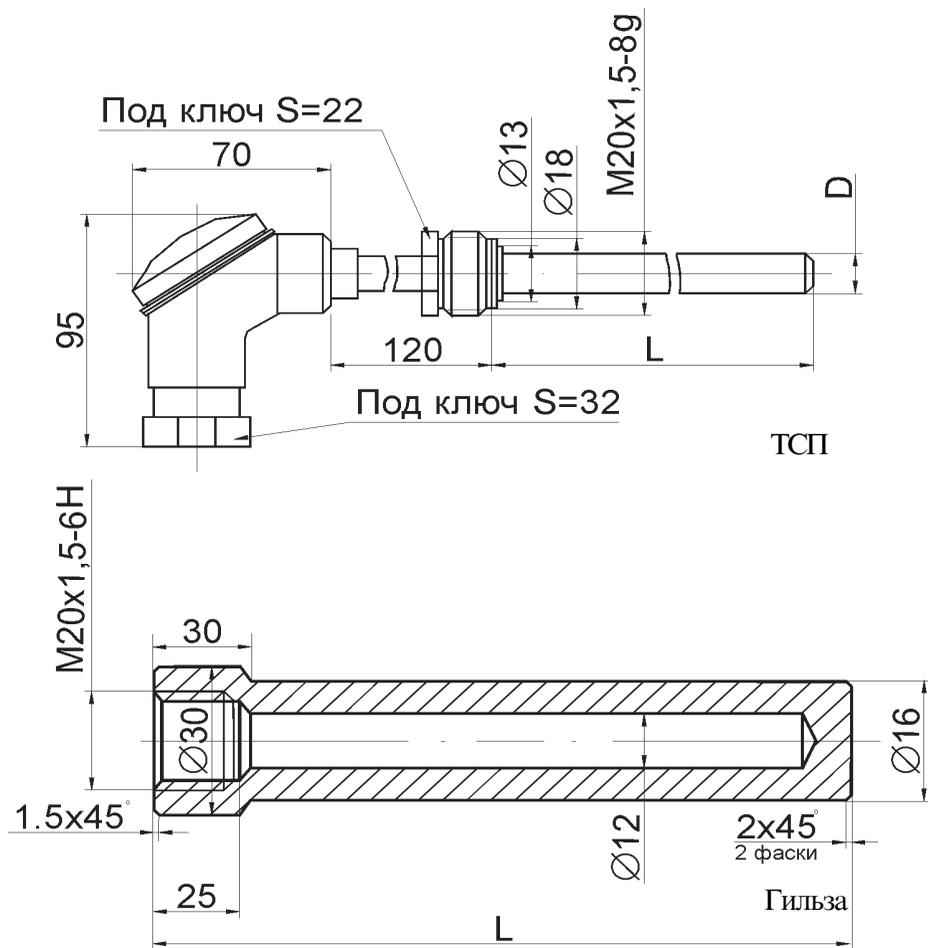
Габаритные и установочные размеры ТСП и защитных гильз
